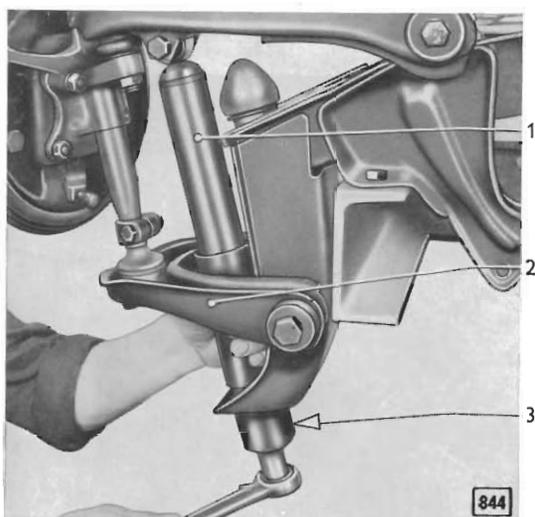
Stoßdämpfer von oberer Stoßdämpferbefestigung abschrauben
